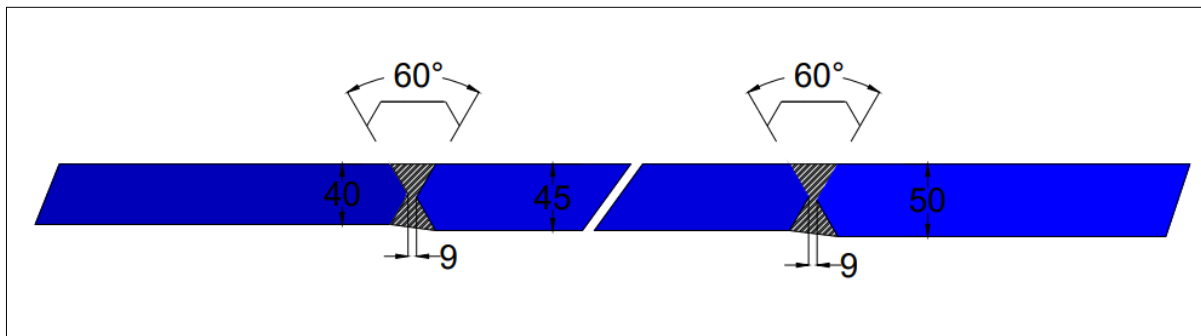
Détail de soudure de la semelle supérieure.
